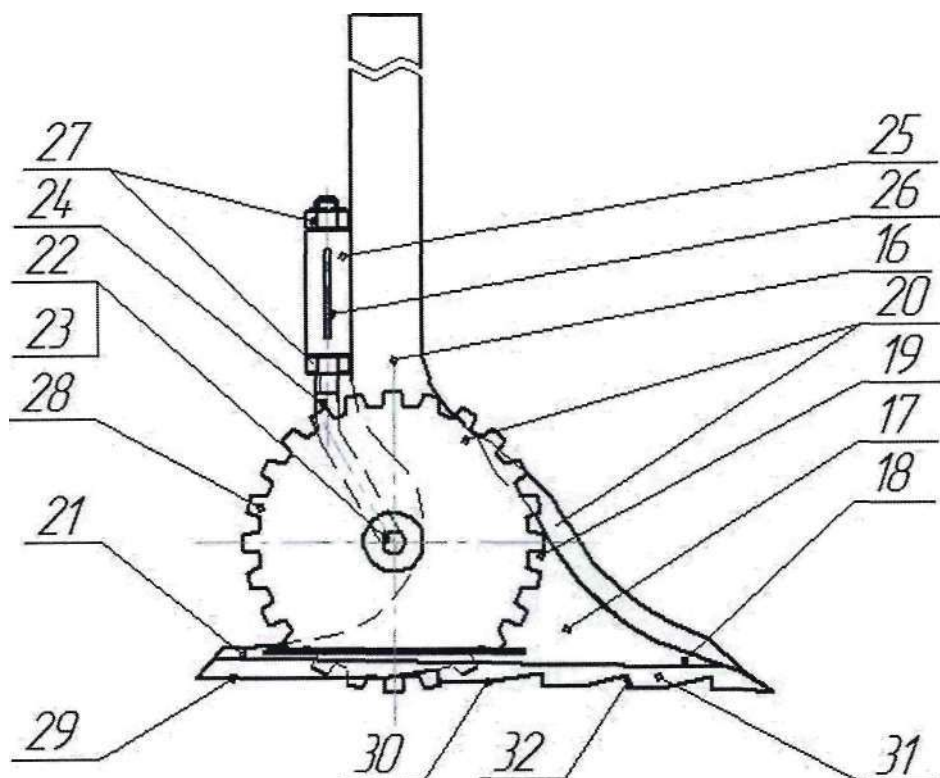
Комбинированный рабочий орган культиватора
